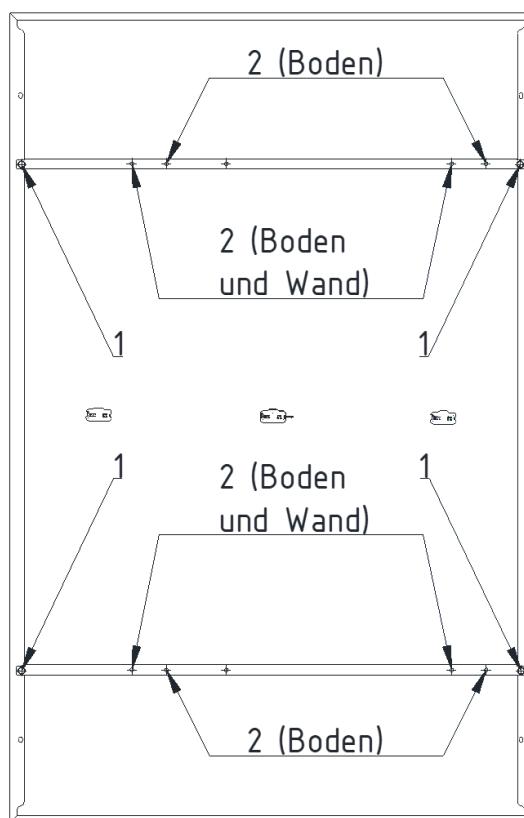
Schraubenpositionen für die Montage auf Standfüßen
